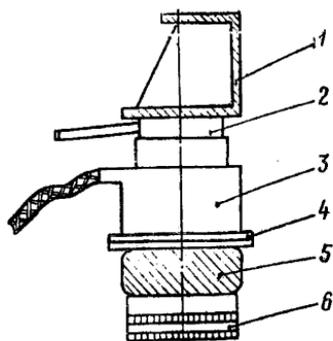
Опрессовка обмотки гидравлическими домкратами:
